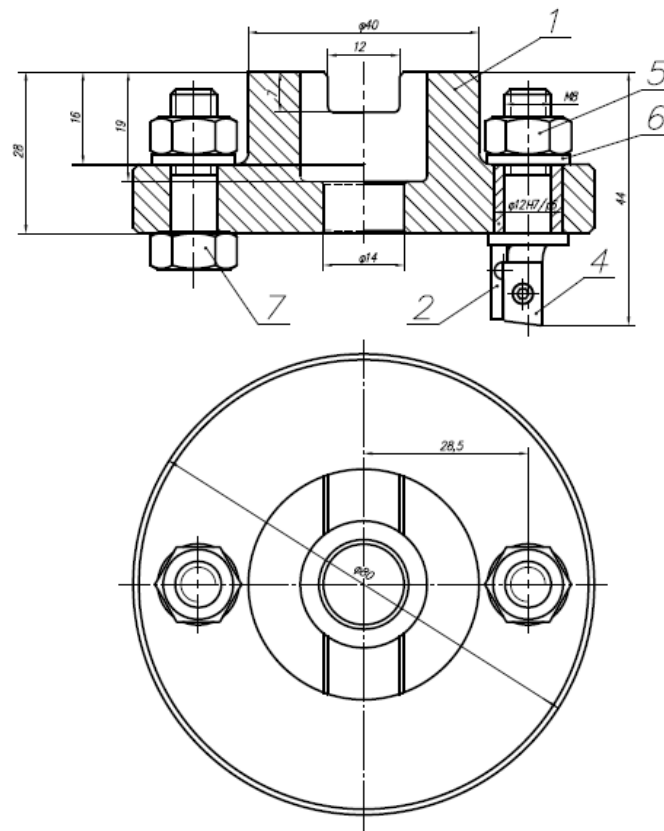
Конструкция торцевой регулируемой фрезы с режущими элементами из СТМ
